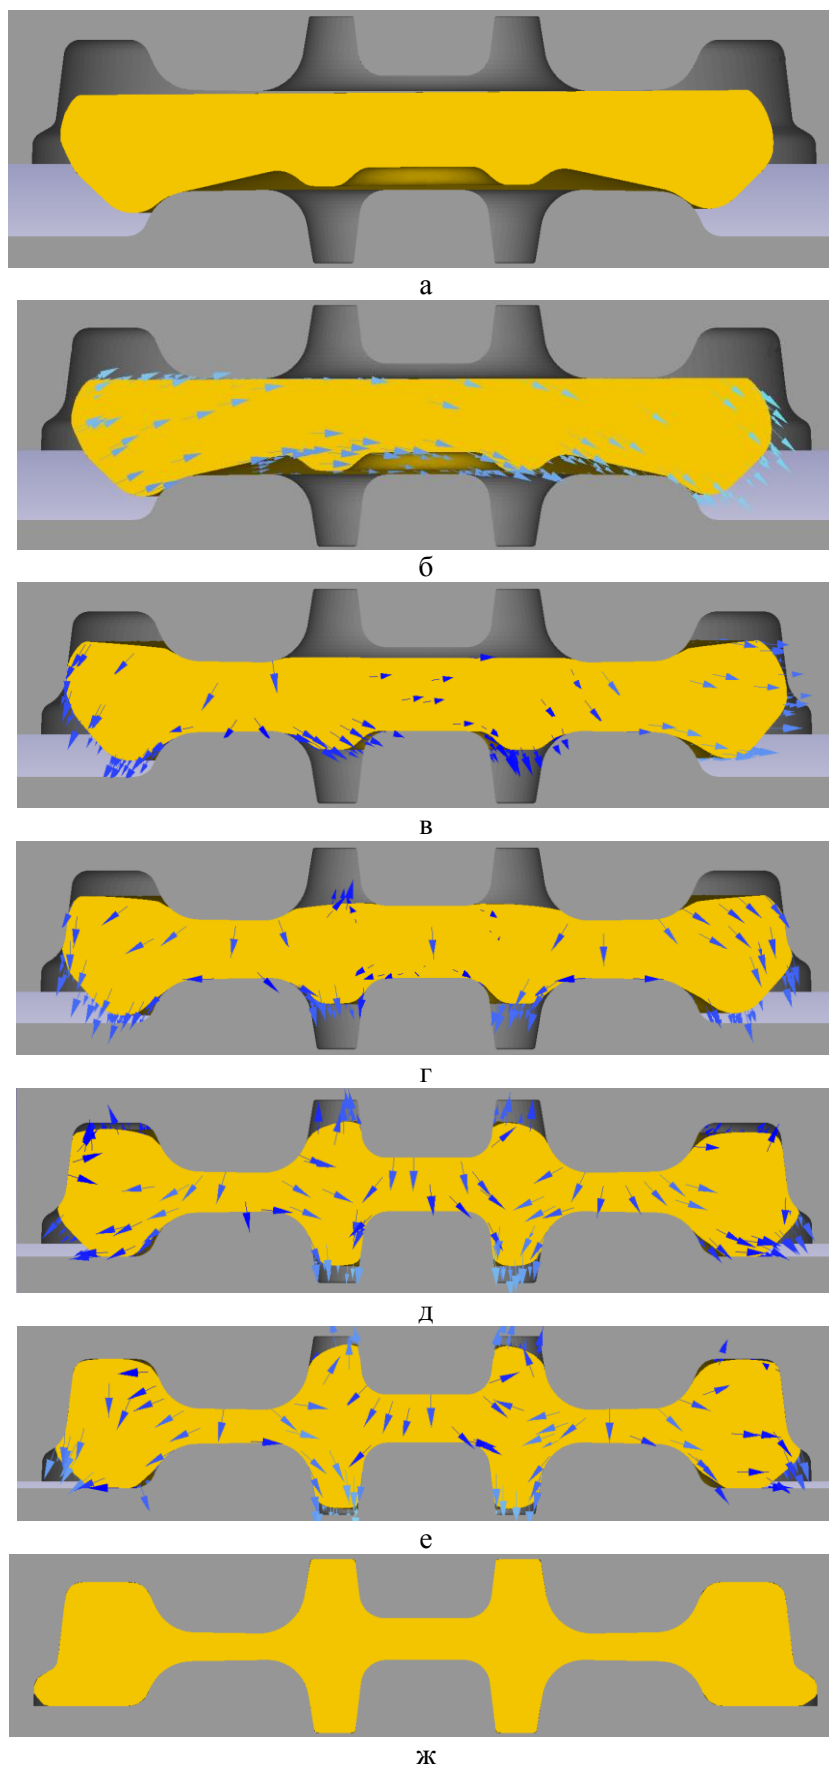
Моделирование процесса формовки колесной заготовки (ось заготовки смещена относительно оси формовочных штампов влево)
